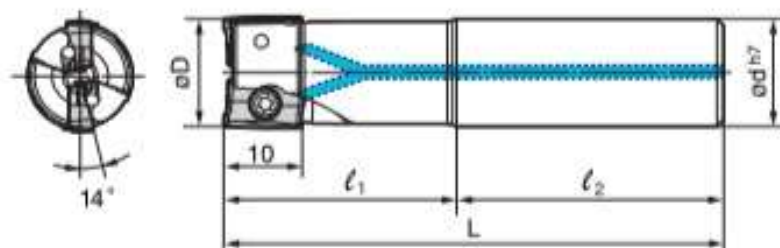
Корпус фрезы Sumitomo для глубокого фрезерования
